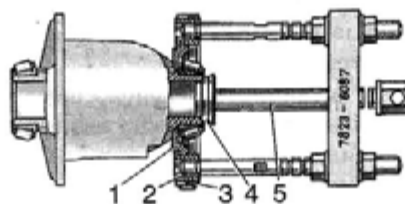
Снятие внутреннего кольца подшипника с коробки дифференциала:
